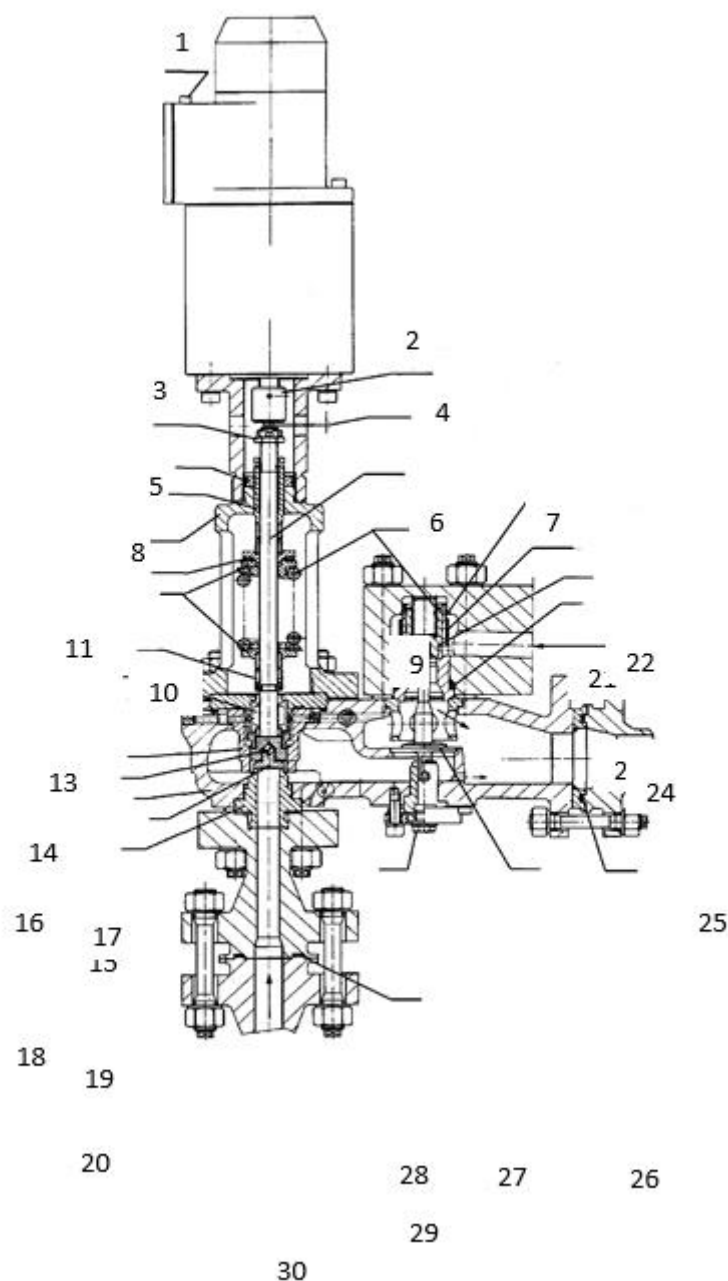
Главный предохранительный клапан ИПУ КД. 1 – колпак защитный, 2 – датчики положения клапана, 3 – постоянный магнит, 4 – указатель положения клапана, 5 – труба, 6 – крышка, 7 – установочная возвратная пружина, 8 – опорная штанга, 9 – прокладка никелевая, 10 – штифт, 11 – главный цилиндр, 12 – сброс пара из разгрузочной полости через импульсный клапан в барботер, 13 – винт установочный, 14 – разгрузочная полость, 15 – наплавка, 16 – кольцо поршневое, 17 – камера “А”, 18 – корпус, 19 – дроссельное отверстие, 20 – диафрагма.
